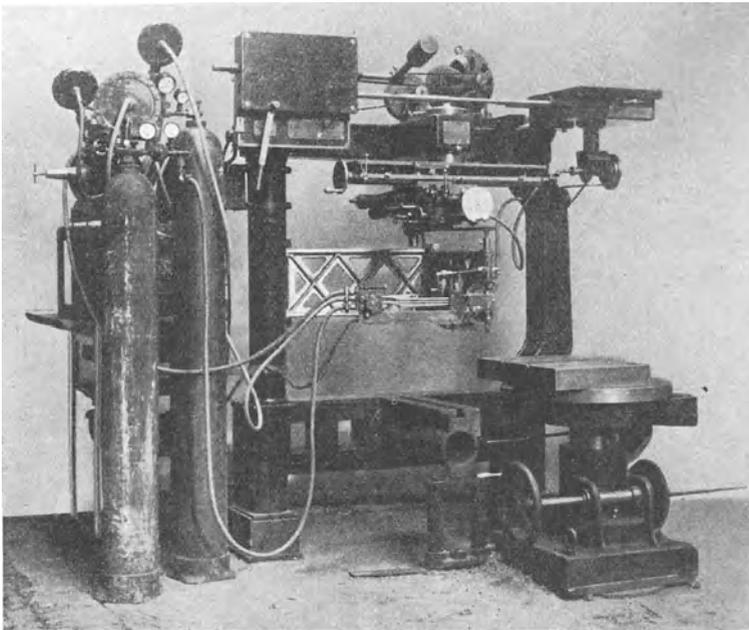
Gesamtansicht der Godfrey-Schneidmaschine.
